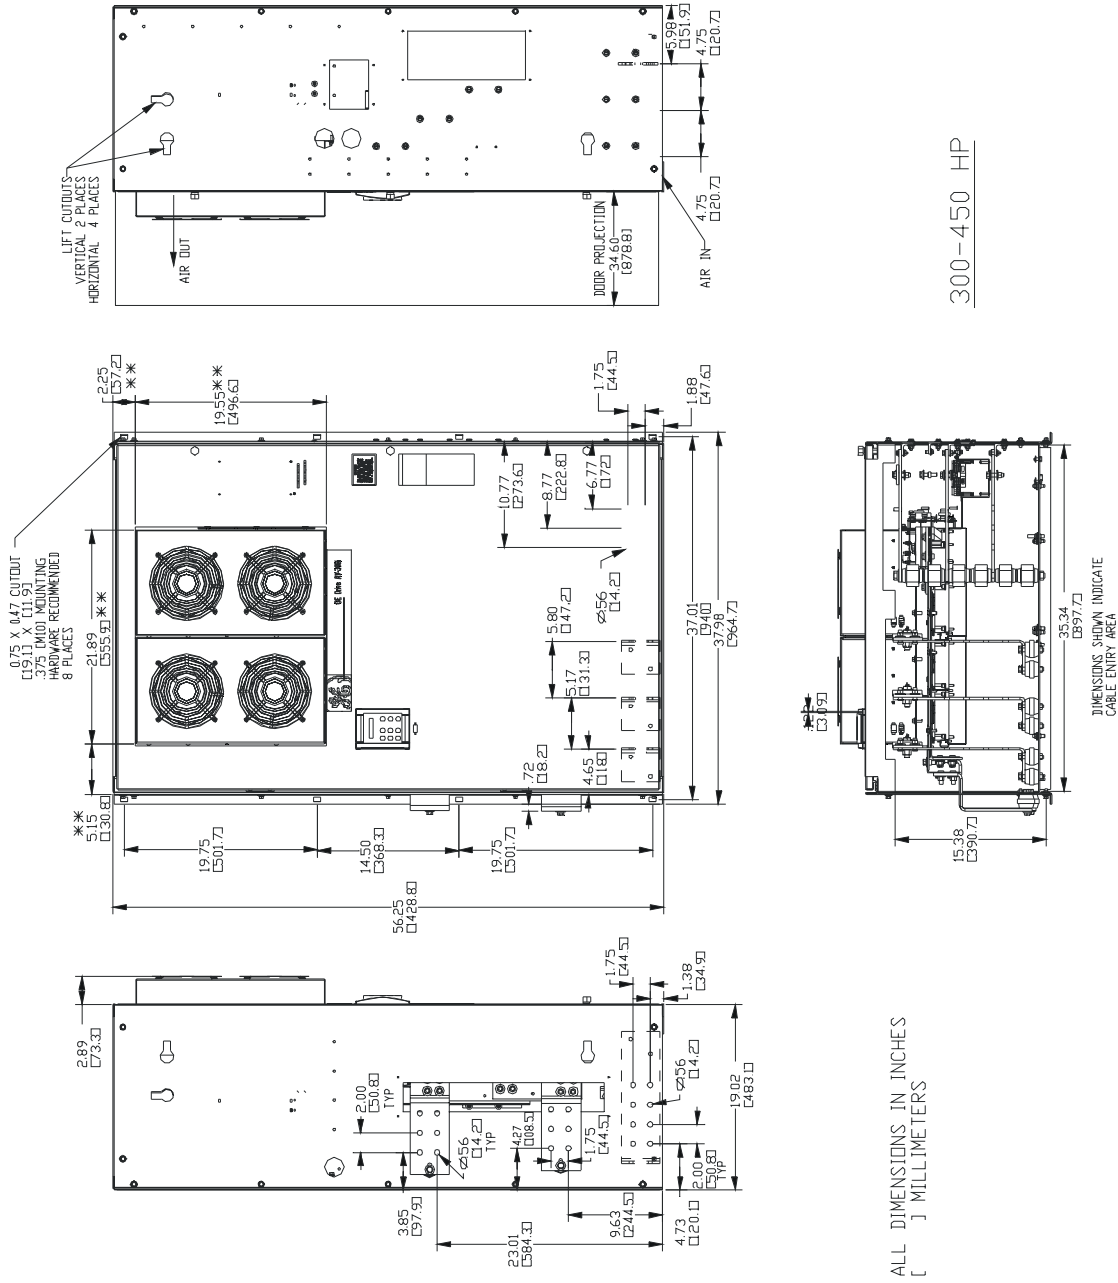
Габаритный чертеж 300 - 450 Лс.
